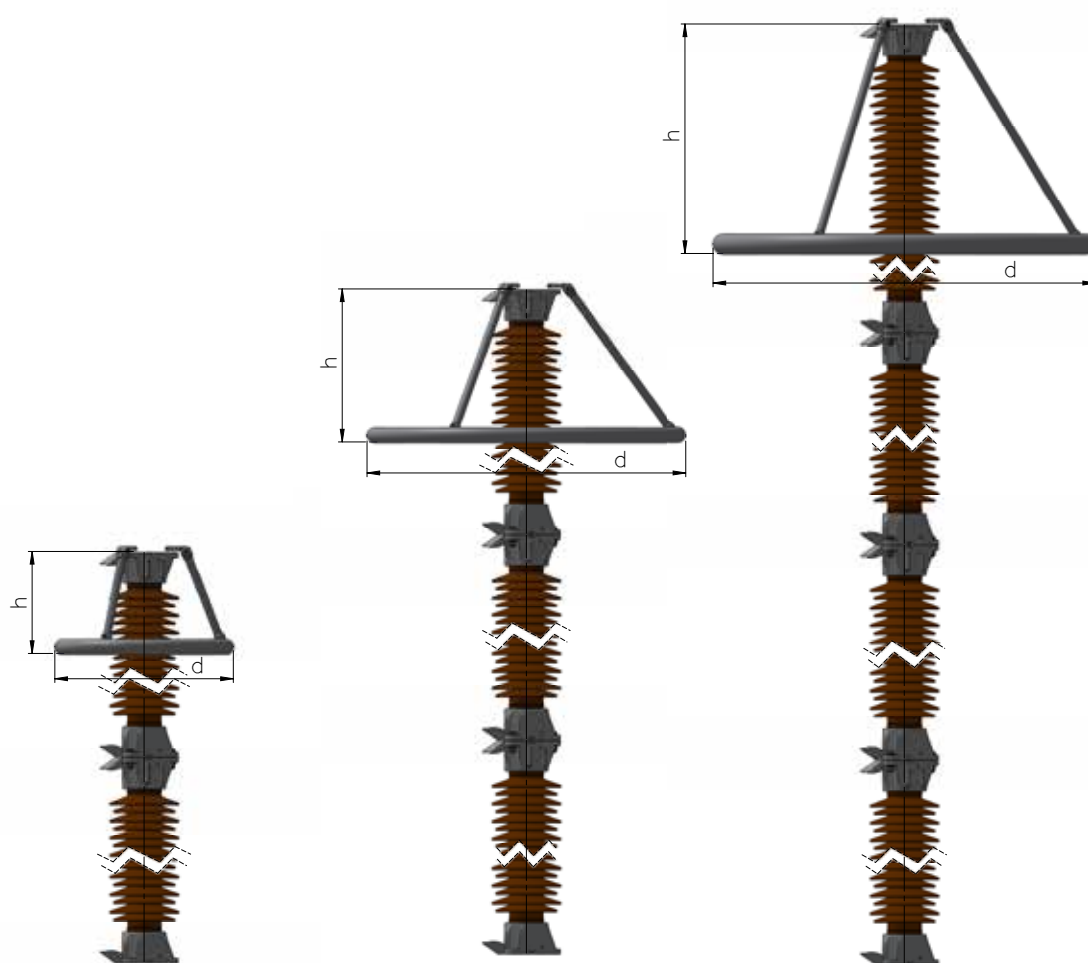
Steuerring-Streben bei Bolzenanschluss
